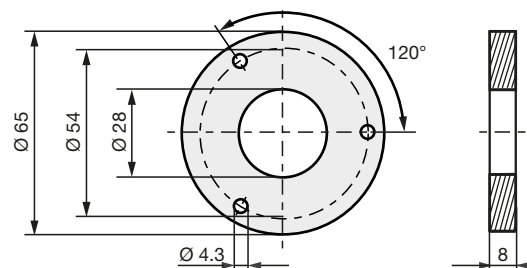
Accessori speciali BTL-P-1028-15R
